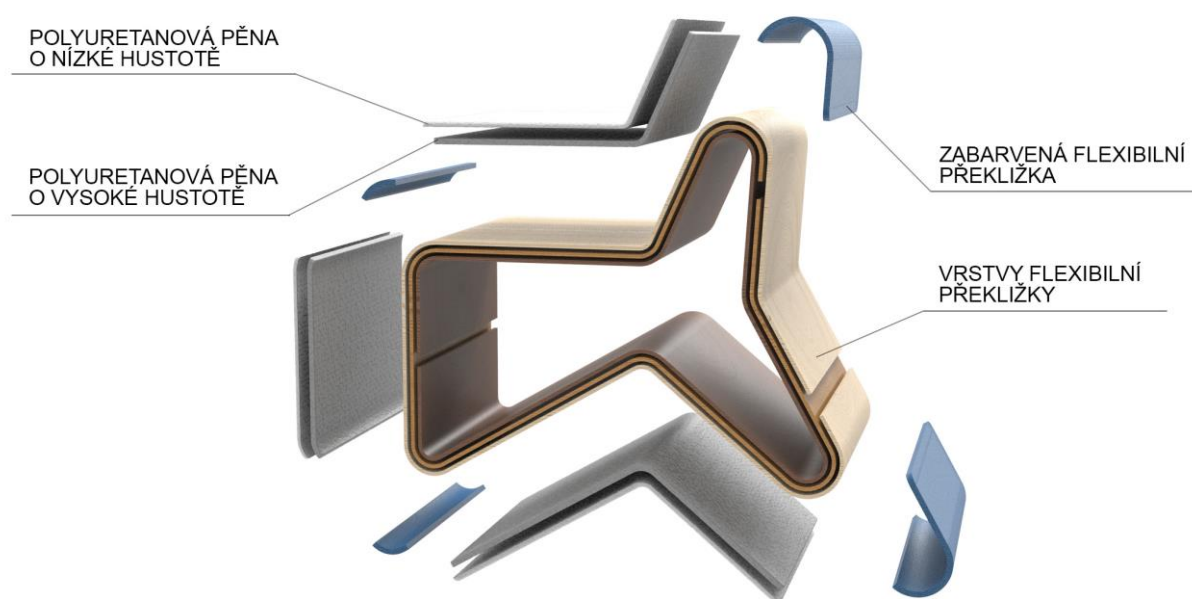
Finální varianta – komponenty pro modulární spojování
